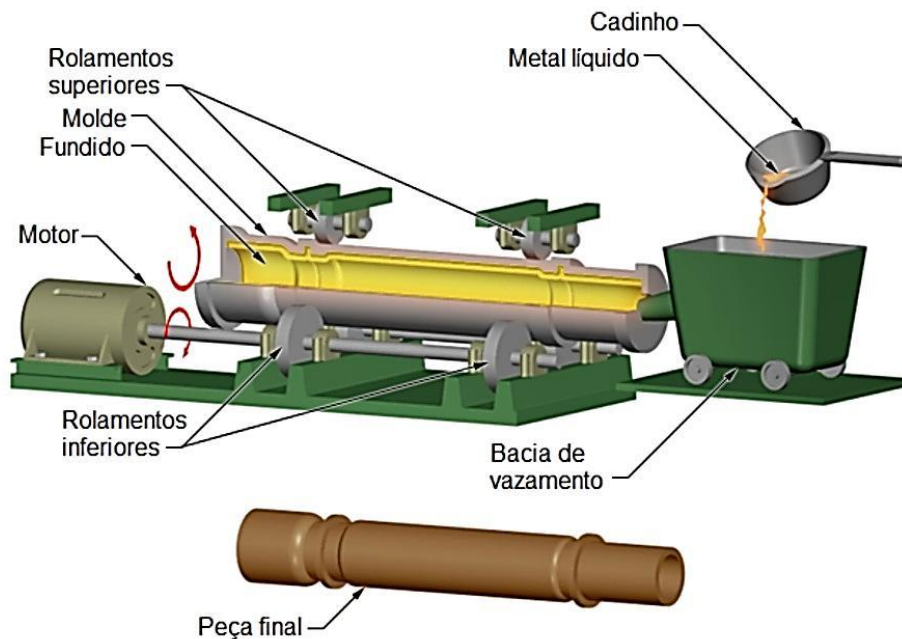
Desenho esquemático de um equipamento convencional de fundição centrífuga horizontal. Adaptado de [39].
